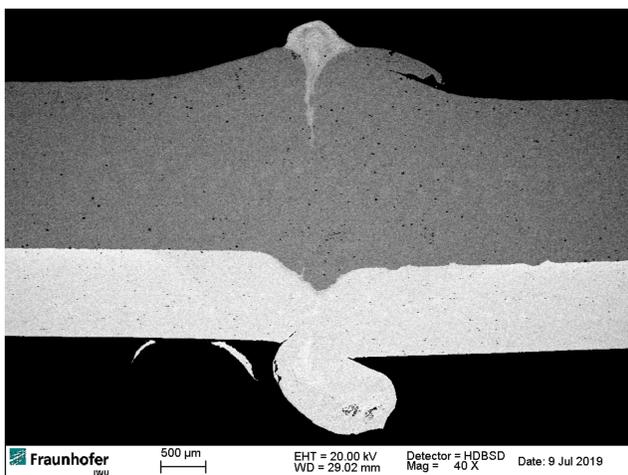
REM-Aufnahme des Fügequerschnitts einer S355/Alloy 625 - Schweißnaht
